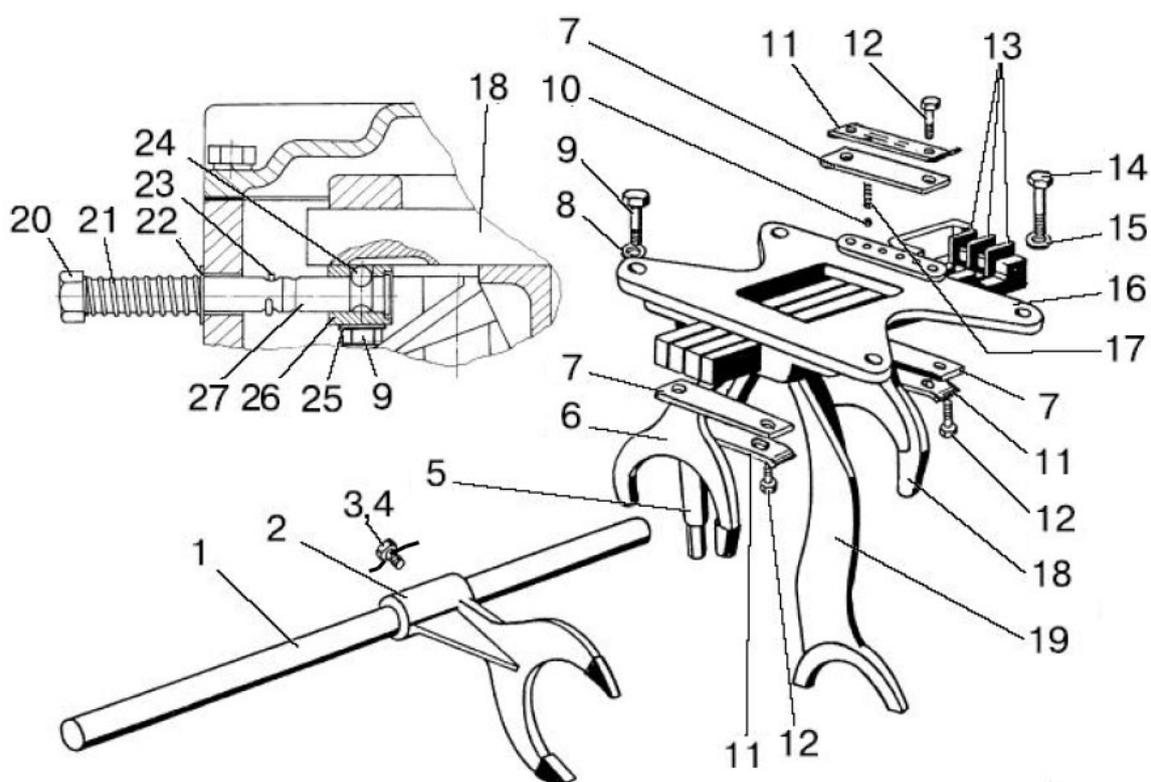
Механизм управления механической КП. Корпус вилок.
